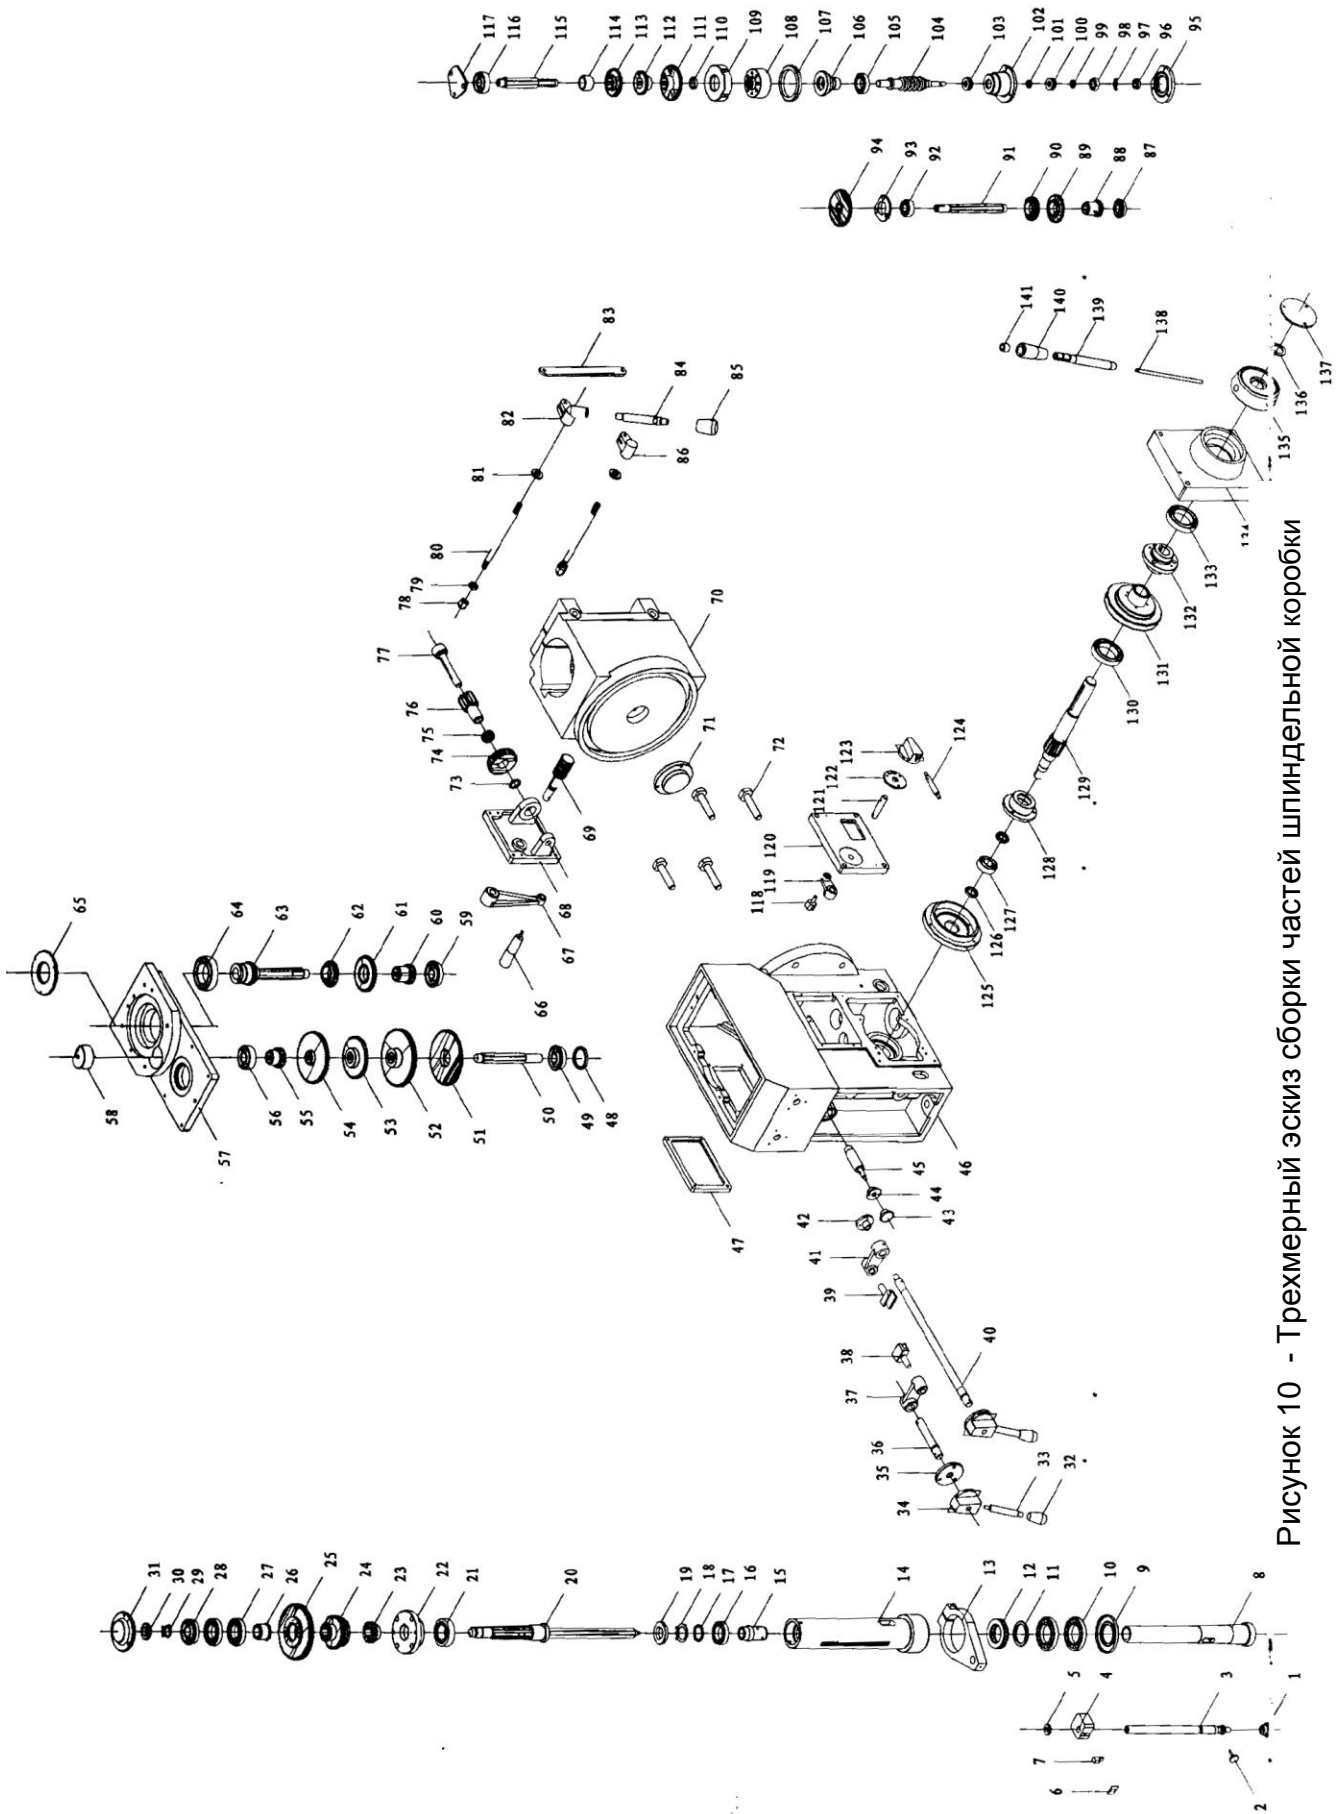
Трехмерный эскиз сборки частей шпиндельной коробки
